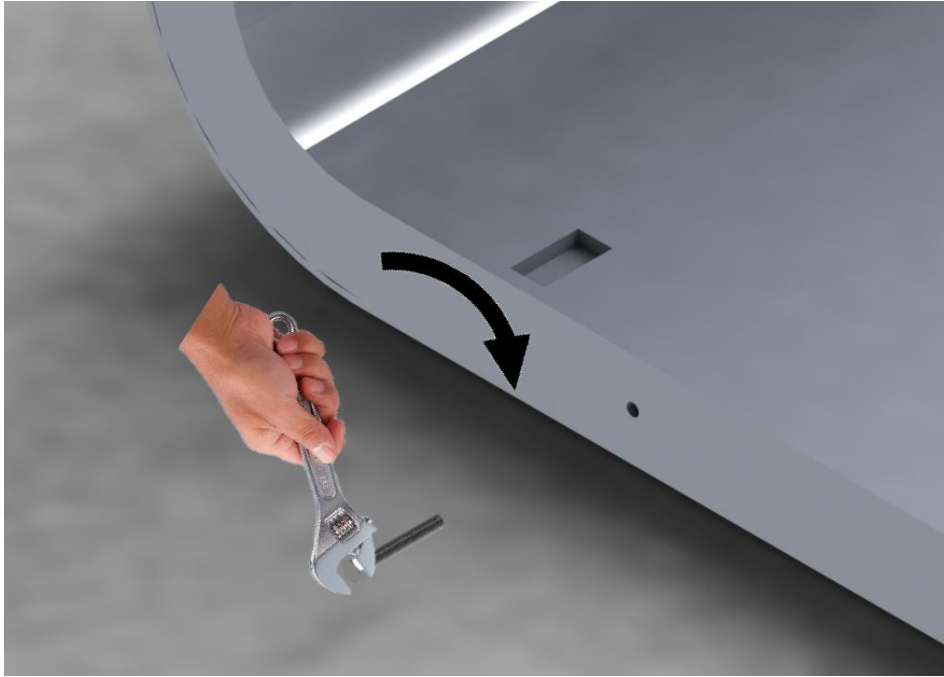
Ensamblaje subconjunto 1. Proceso de giro con llave M8x60.
